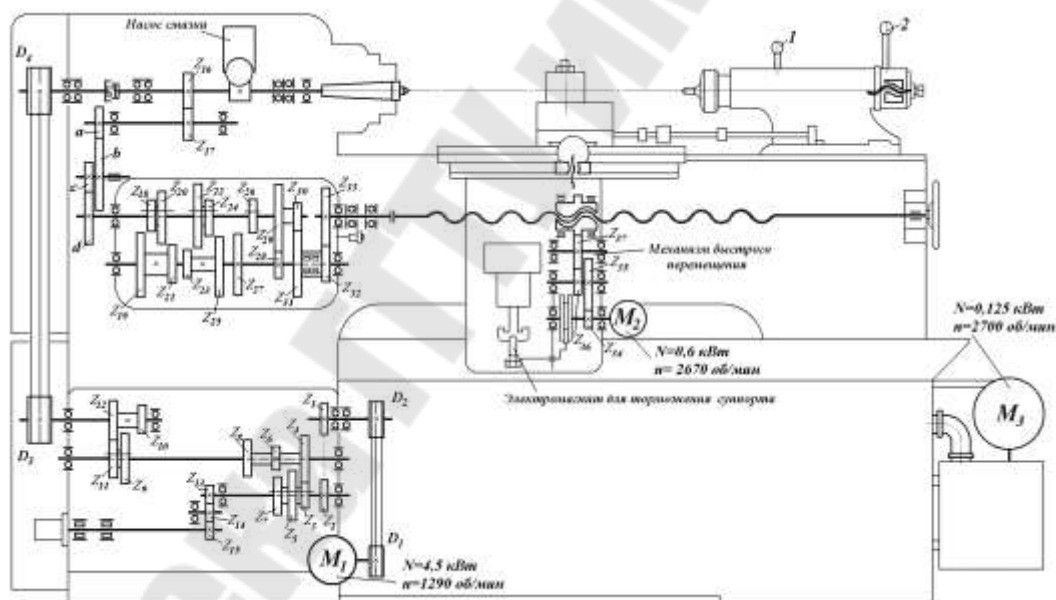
Кинематическая схема токарного полуавтомата модели КТ-16
